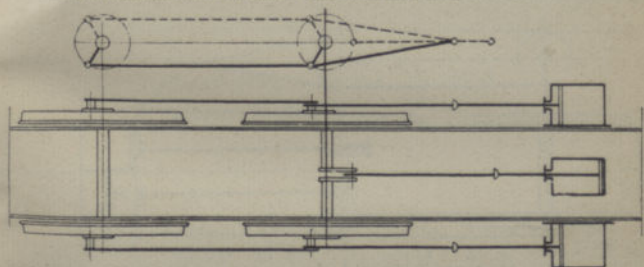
Mechanismo motor de simples expansão, com 3 cylindros.
